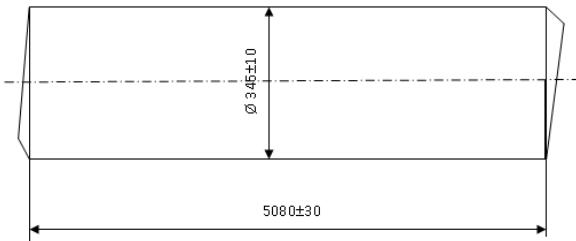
Эскиз поковки для детали «Дорн 12»
